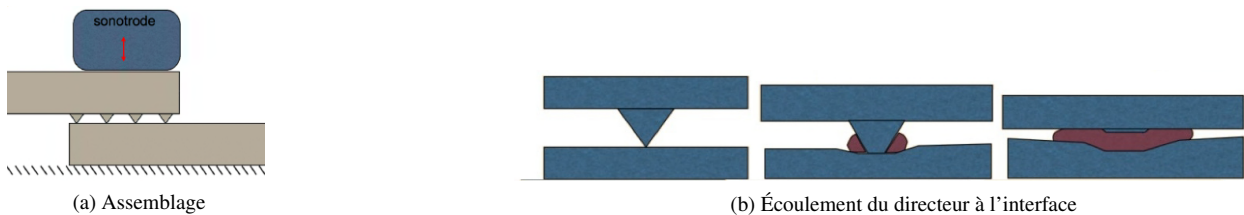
Soudage par ultrasons de deux plaques
